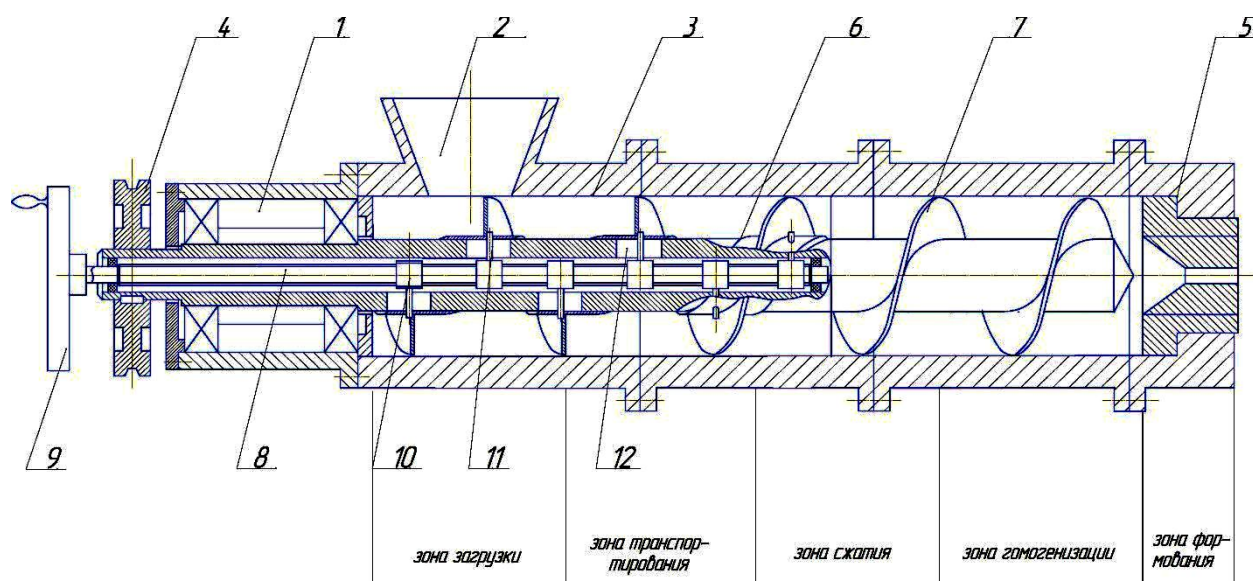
Конструкция одношнекового пресс-экструдера:
